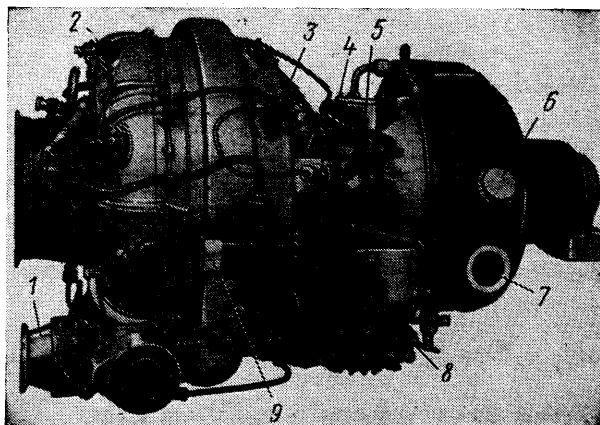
Расположение агрегатов на двигателе (вид справа):
